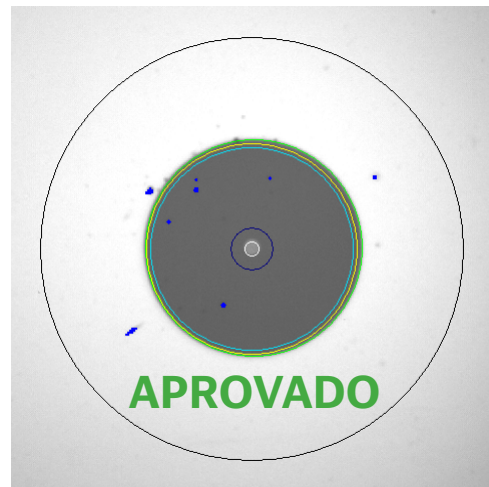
A inspeção automatizada dá aos técnicos um resultado de aprovado ou reprovado.
